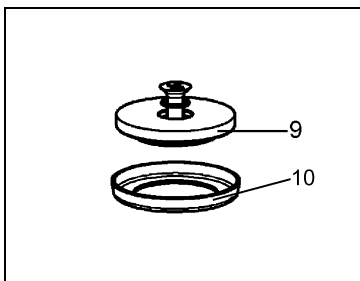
Ausrichtung der Dichtlippe (10) zu Druckscheibe (9)
